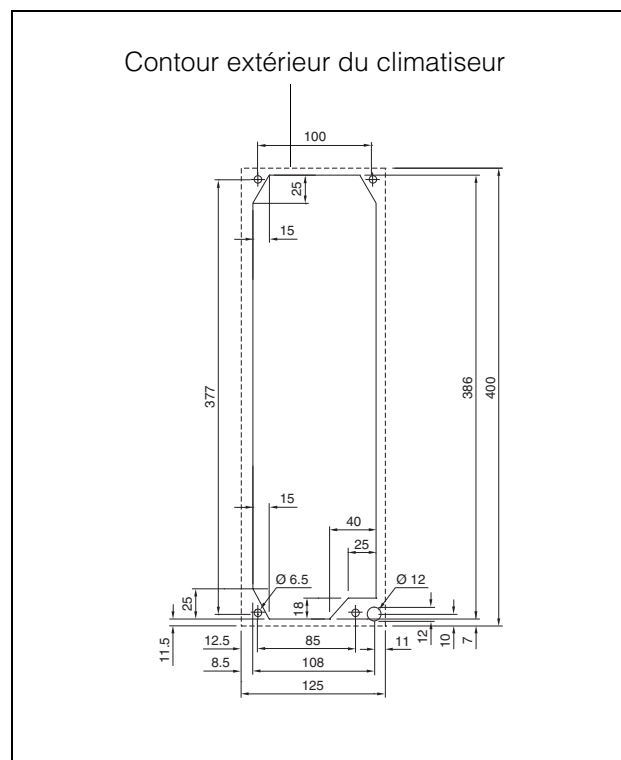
Découpe de montage et dimensions des perçages pour l'encastrement complet de l'appareil
